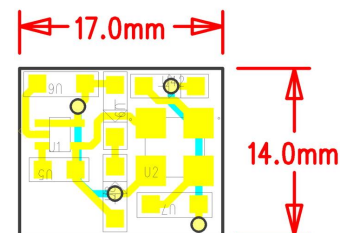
소형 DC-DC 컨버터의 PCB Layout
